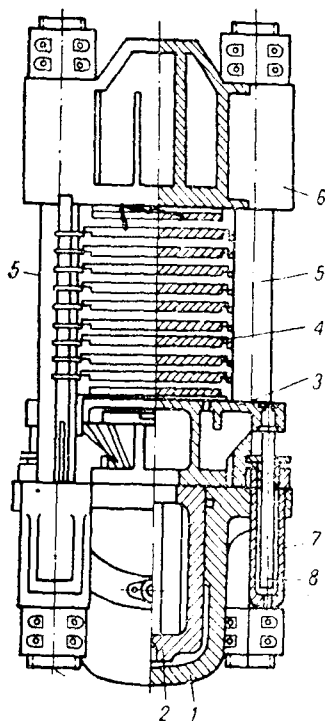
Плиточный этажный гидравлический пресс: 1 — рабочий цилиндр; 2 — рабочий плунжер; 3 — подвижной стол; 4 — плиты; 5 — колонны; 6 — архитрав; 7, 8 — вспомогательный цилиндр.
